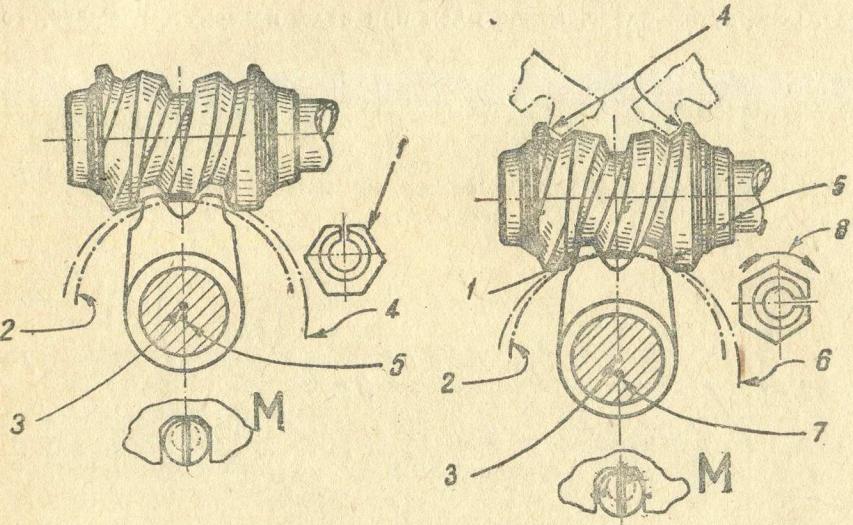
Положение эксцентричной втулки в начале сборки руля.
